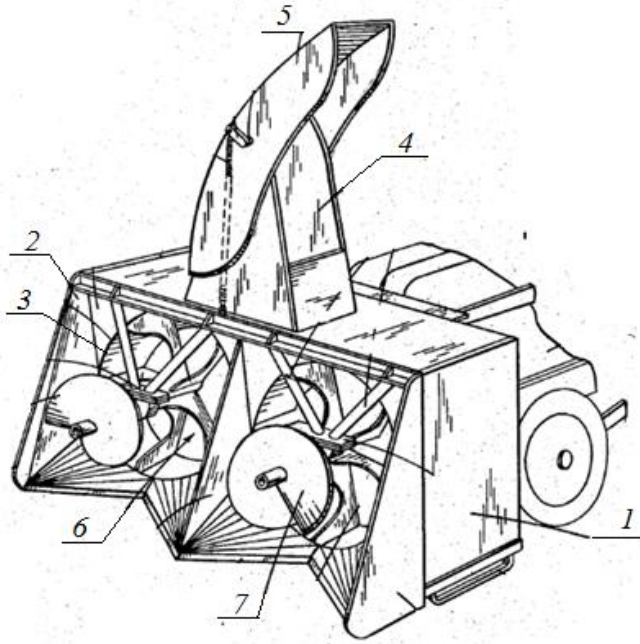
Общий вид снегоочистителя, где 1 – корпус; 2 – съемная секция; 3 – круглая камера; 4 – направляющий желоб; 5 – поворотный кожух; 6 – ротор метательного аппарата; 7 –
